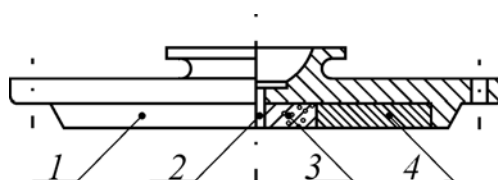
Торцевая крышка центробежной изложницы: 1 – корпус; 2 – отверстие для выхода газов; 3 – кольцевая вставка; 4 – футеровка
